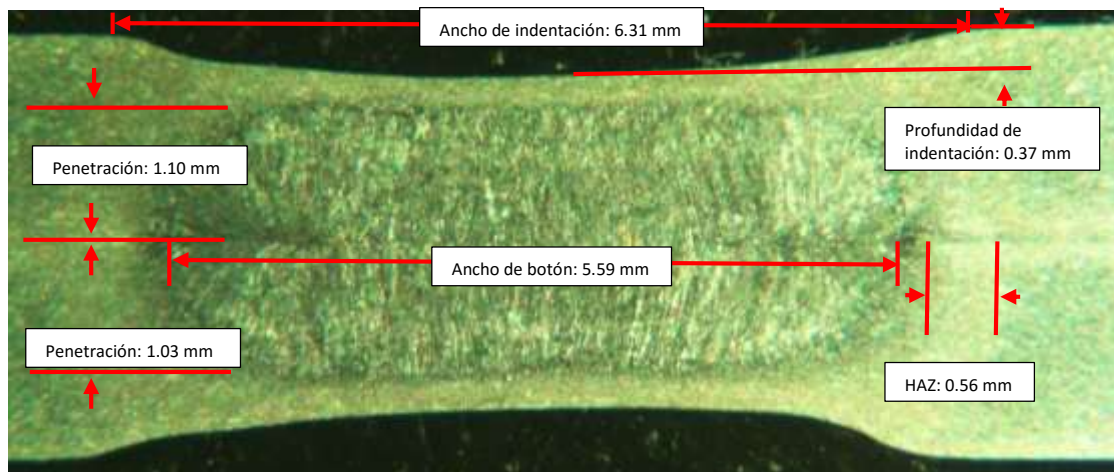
Mediciones realizadas en el botón de soldadura número 10.
